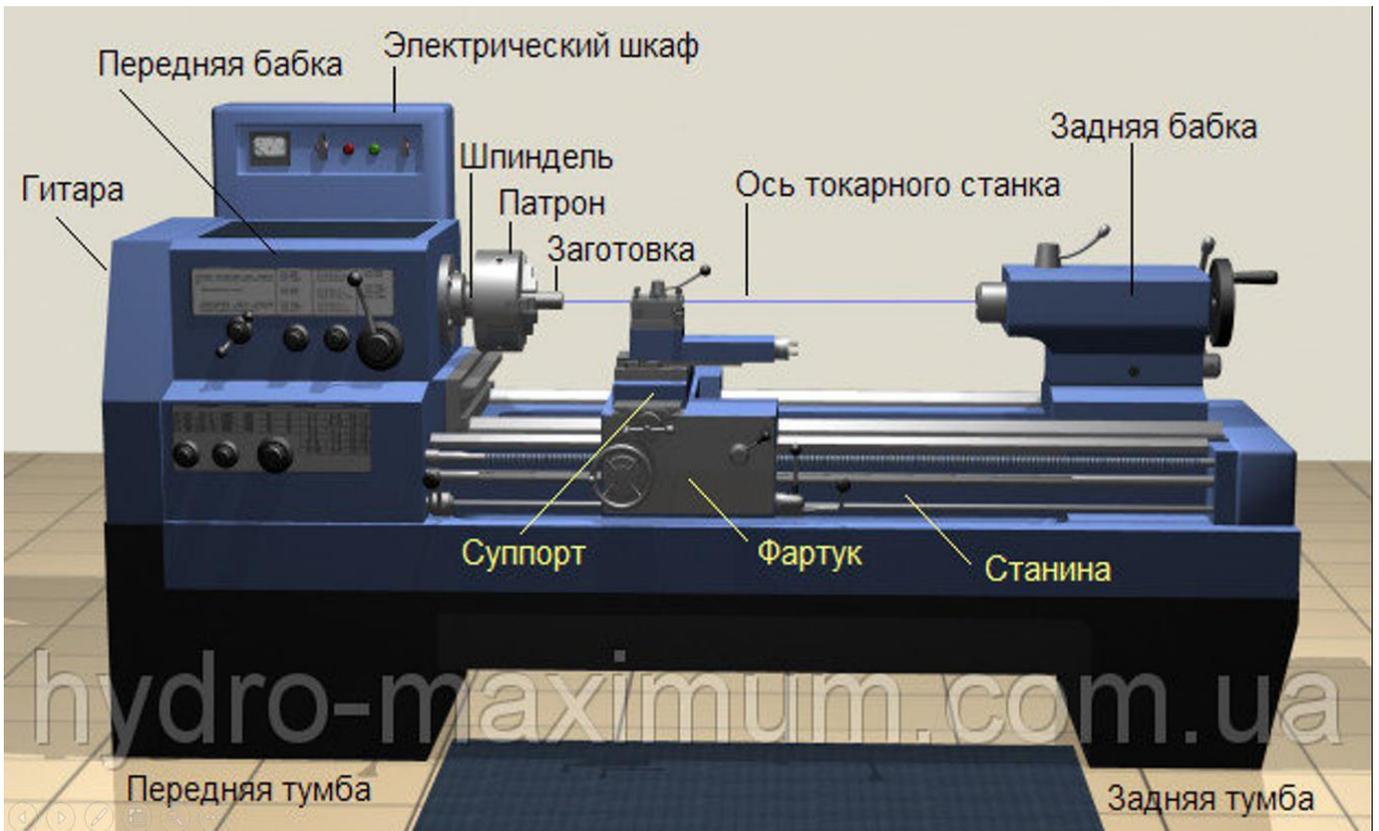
Общий вид токарного станка с указанием основных узлов
